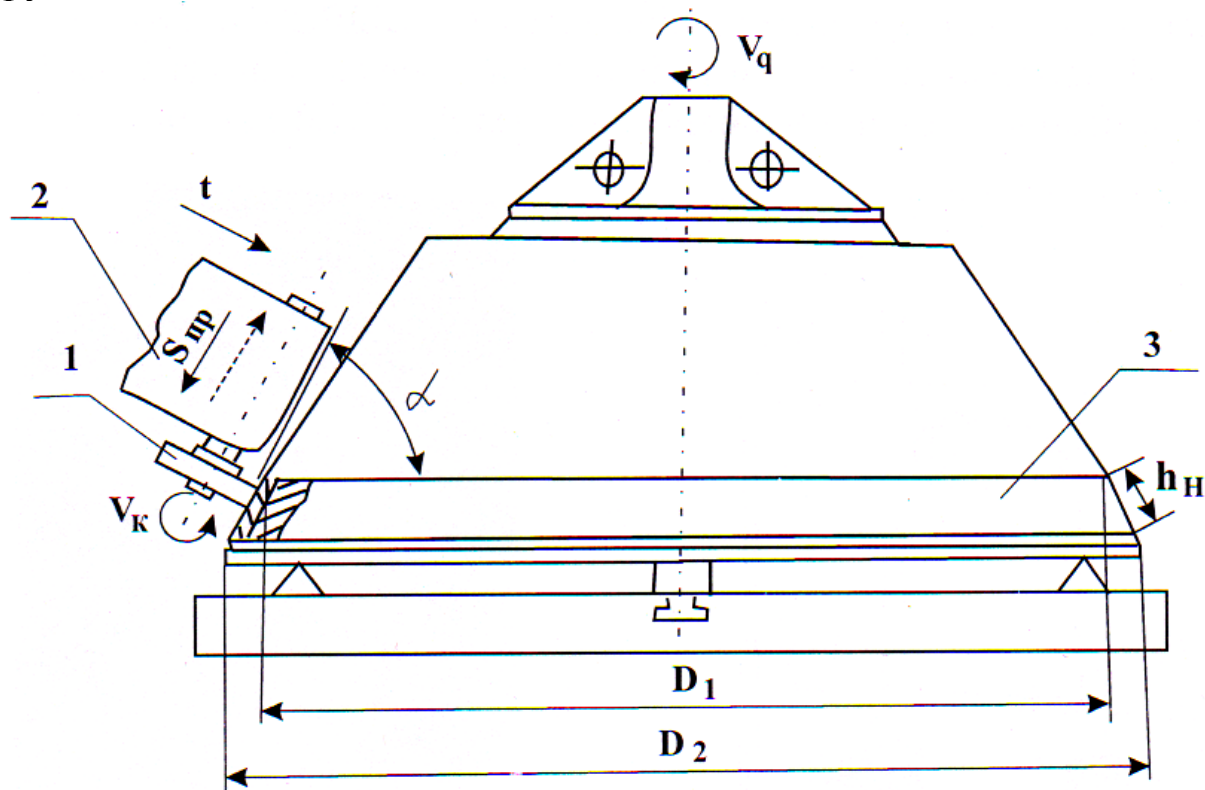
Схема алмазного шлифования фасонной рабочей поверхности большого конуса:
